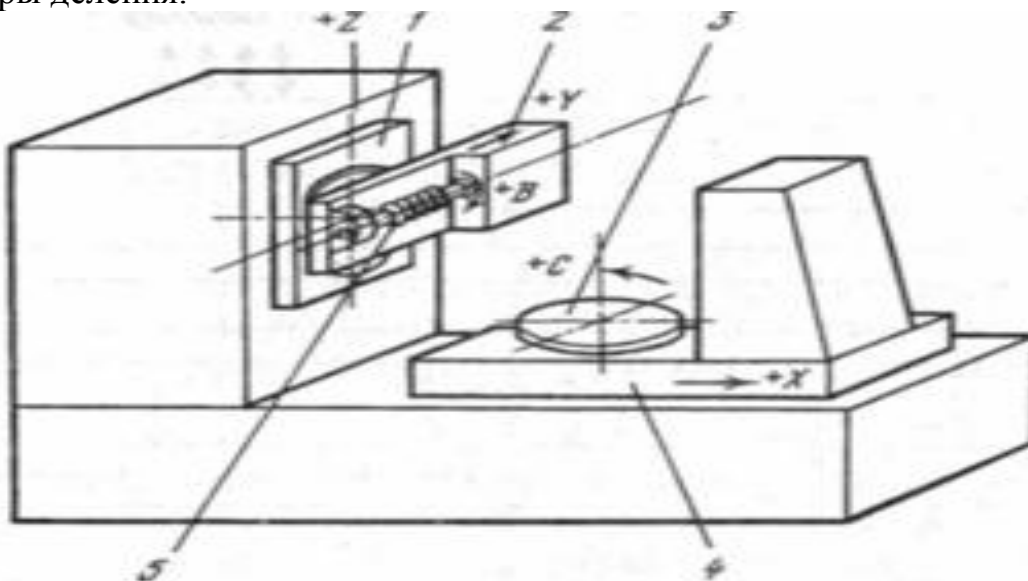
Компоновка станка модели 53А50КФ4
